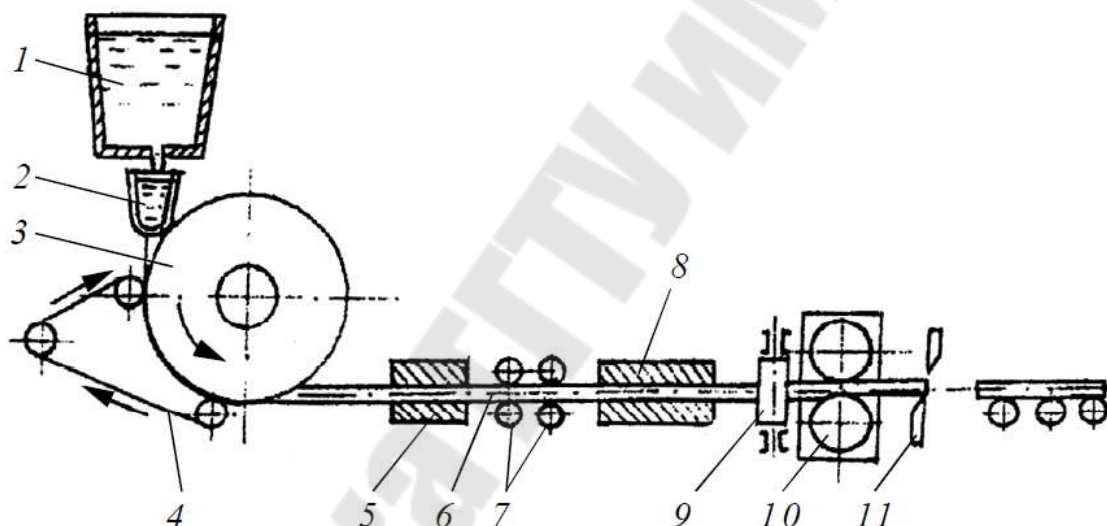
Схема литейно-прокатного агрегата для получения сортового проката:
